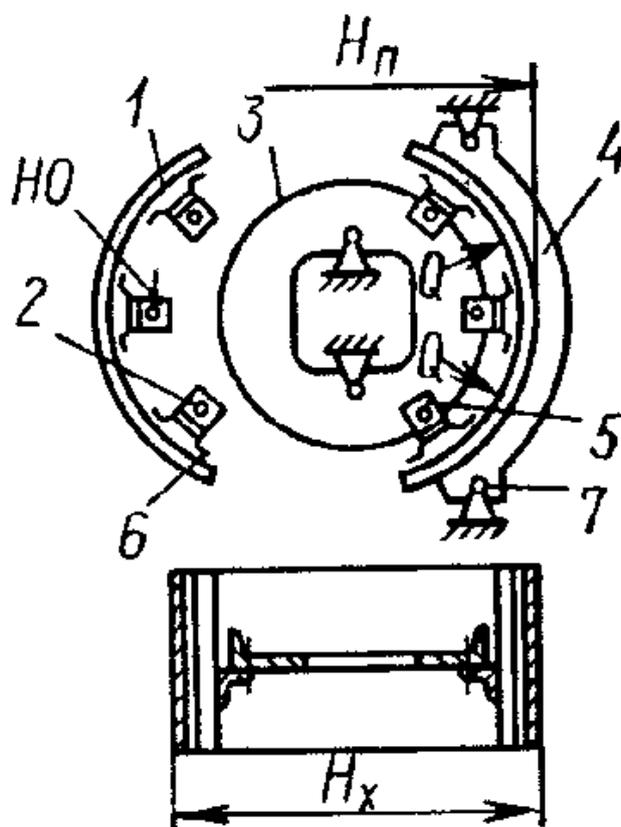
Сборка с базой «Наружная поверхность обшивки»:
